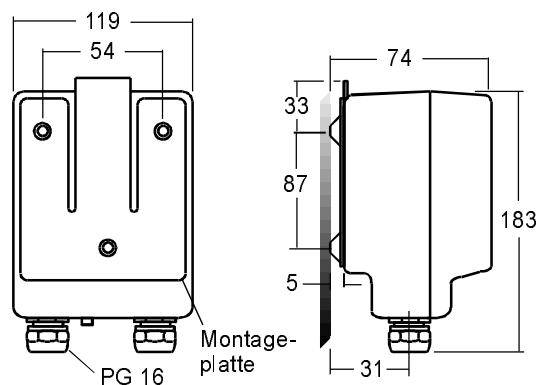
Meßumformer HMI 361 im separaten Gehäuse
